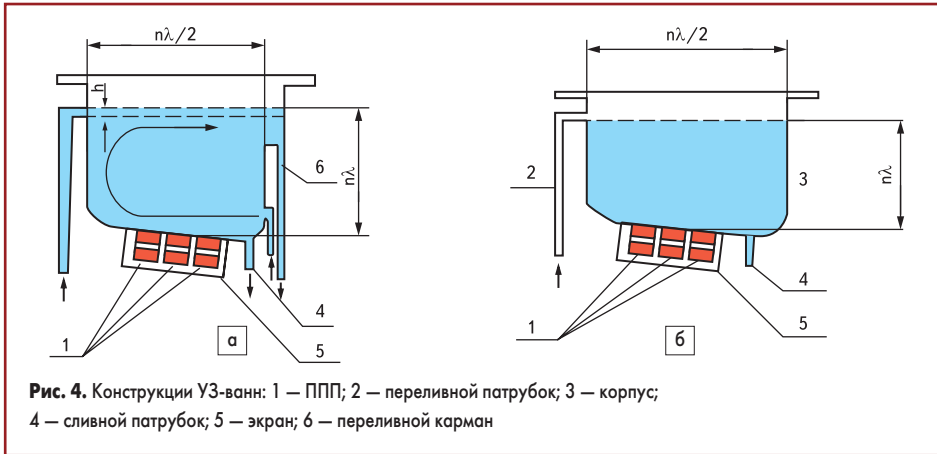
Конструкции УЗ-ванн: 1 — ППП; 2 — переливной патрубком; 3 — корпус; 4 — сливной патрубком; 5 — экран; 6 — переливной карман
